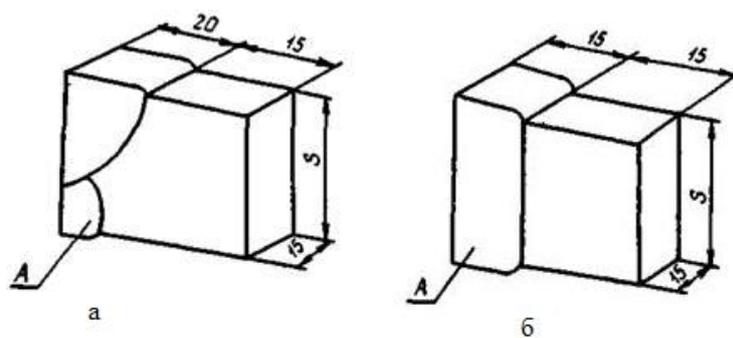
Образец сварного соединения для микроисследования при толщине стенки изделия более 30 мм: а - часть сварного соединения, выполненного ручной, полуавтоматической или автоматической сваркой; б - часть сварного соединения, выполненного электродуговой сваркой; А - исследуемая поверхность микрошлифа; S - толщина стенки изделия
